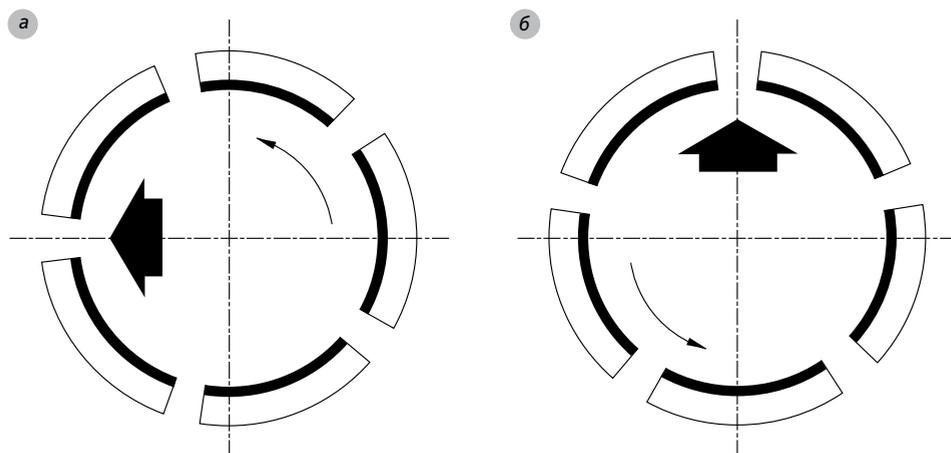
Реакция на нагрузку: а) опорного подшипника № 3; б) опорно-упорного подшипника № 4
